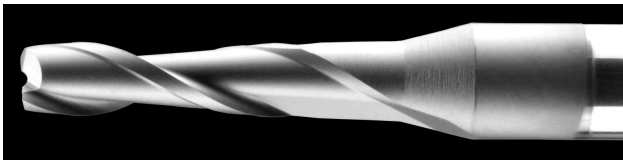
Diamant beschichteter 2-Schneidenfräser - GCT Typ 1322
